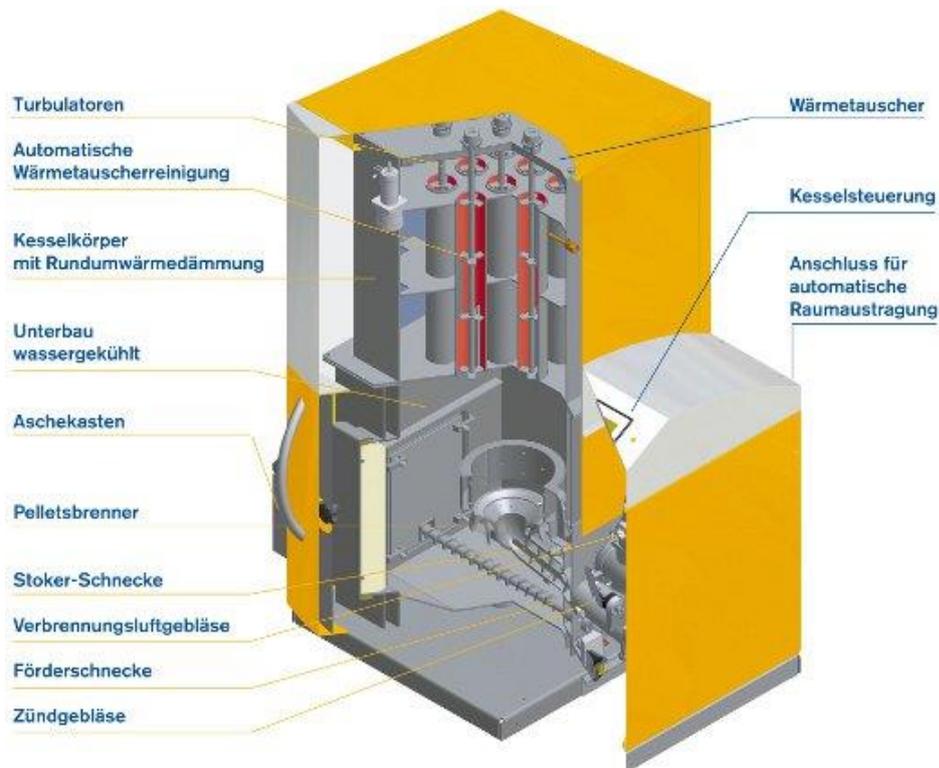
Aufbau eines Pelletkessels, © Bosch Thermotechnik GmbH (Junkers)
